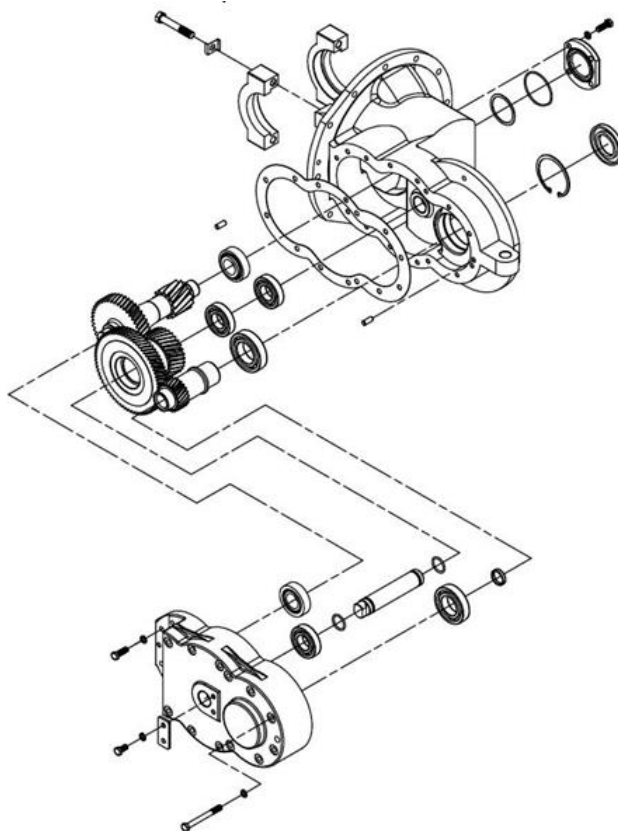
Схема конструкции редуктора вилочного погрузчика.
